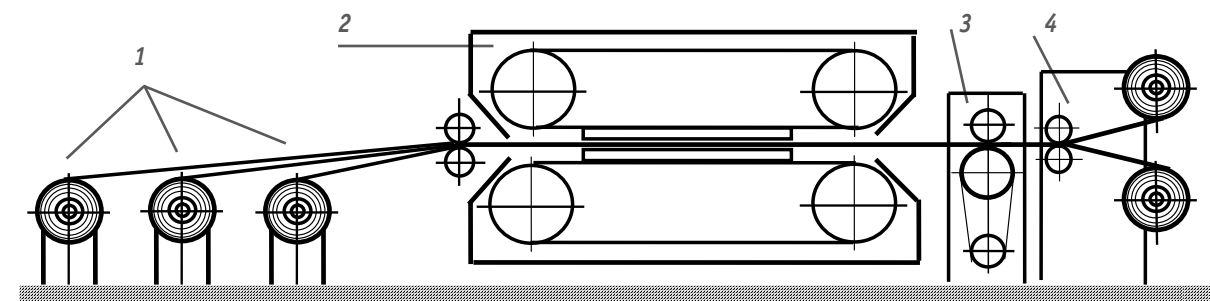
Схема установки для ламинирования на базе ленточного пресса
